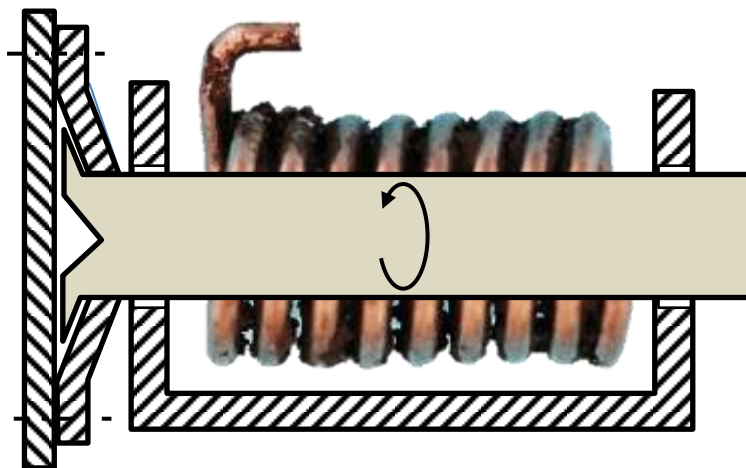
Drehbolzen zwischen Flansch und Gehäuse befestigt
